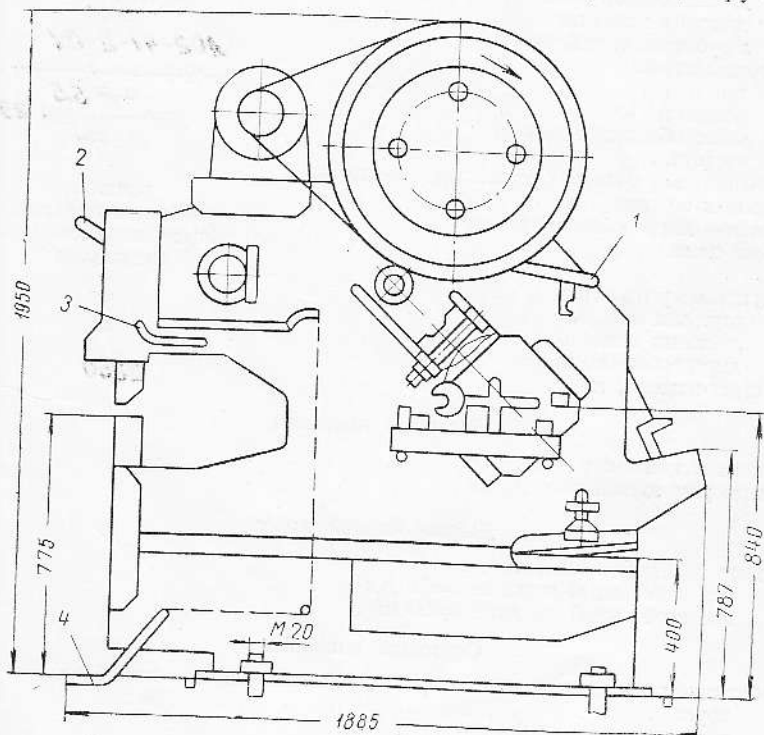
Общий вид пресс-ножниц и габаритные размеры:
